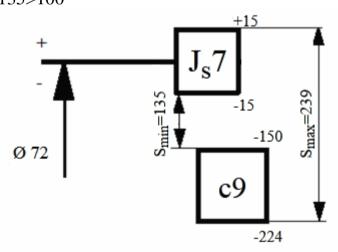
Выбор посадки для сопряжения крышки и отверстия корпуса
